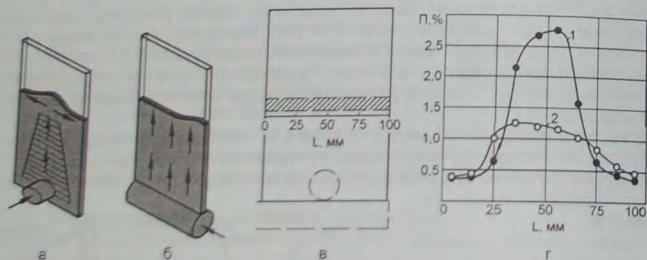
Схемы заполнения рабочих полостей КО расплавом (а, б), схема вырезки образцов (в) и распределение пористости по ширине плоской отливки (г) из стали 08X14H7МЛ: 1 — для отливок, полученных с нижним питателем точечного типа (а); 2 — для отливок, полученных с нижним питателем щелевого типа (б)
